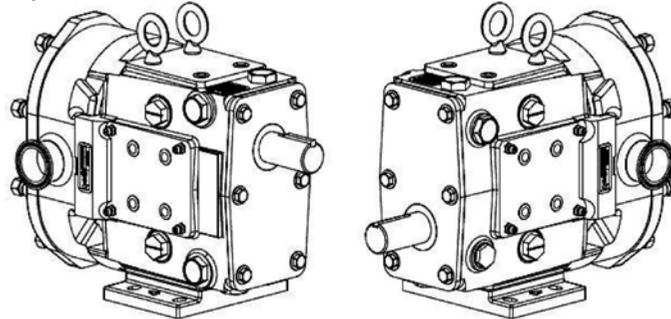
Montajes de la flecha motriz posiciones superior e inferior
